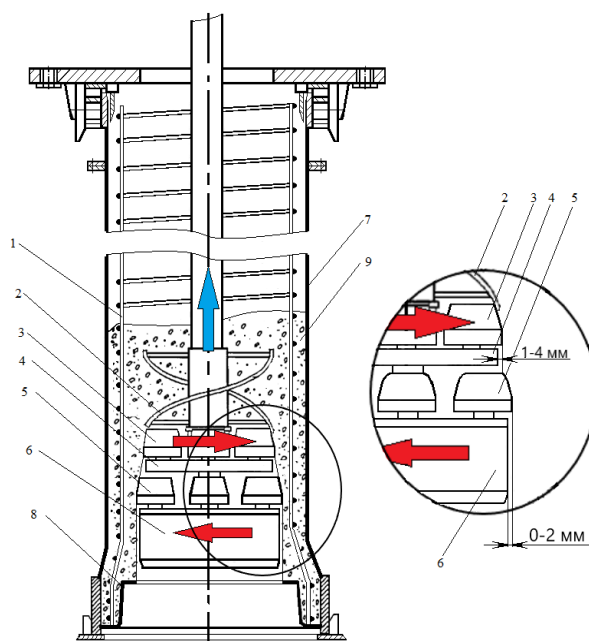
Схема формования железобетонной трубы методом радиального прессования:
